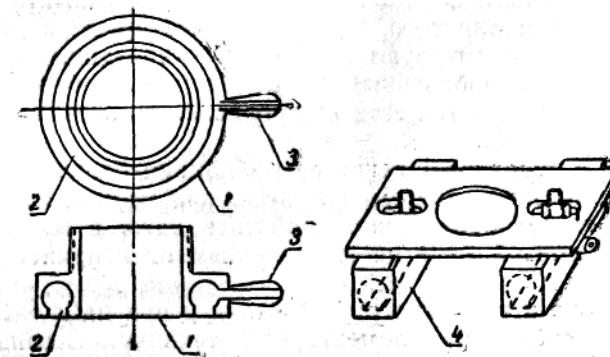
Разрядно-оптическая обкладка с приспособлением для растягивания поверхности кожного покрова.
